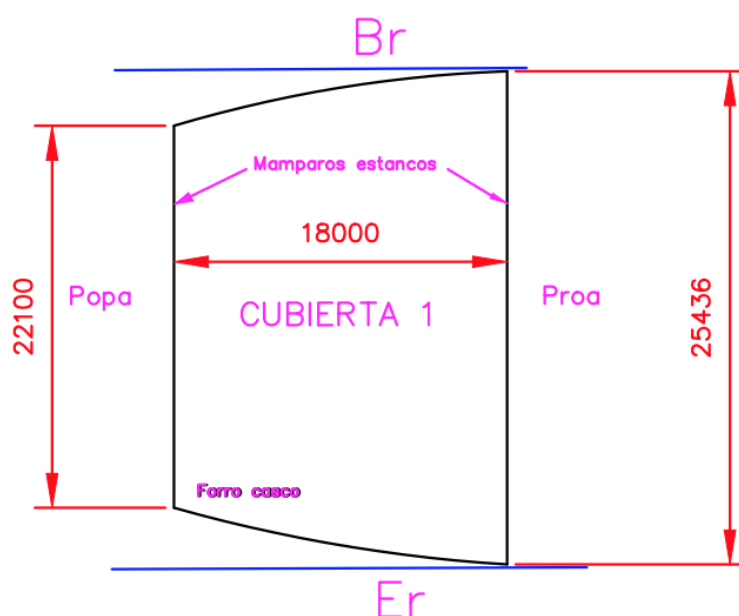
Vista planta Cubierta 1. Elaboración propia AutoCad.
